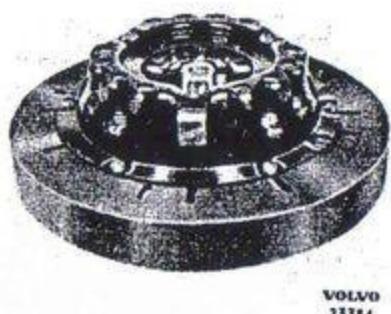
Kopplingen monterad på universaljiggen SVO 1077 A med justerjiggen SVO 2066.
